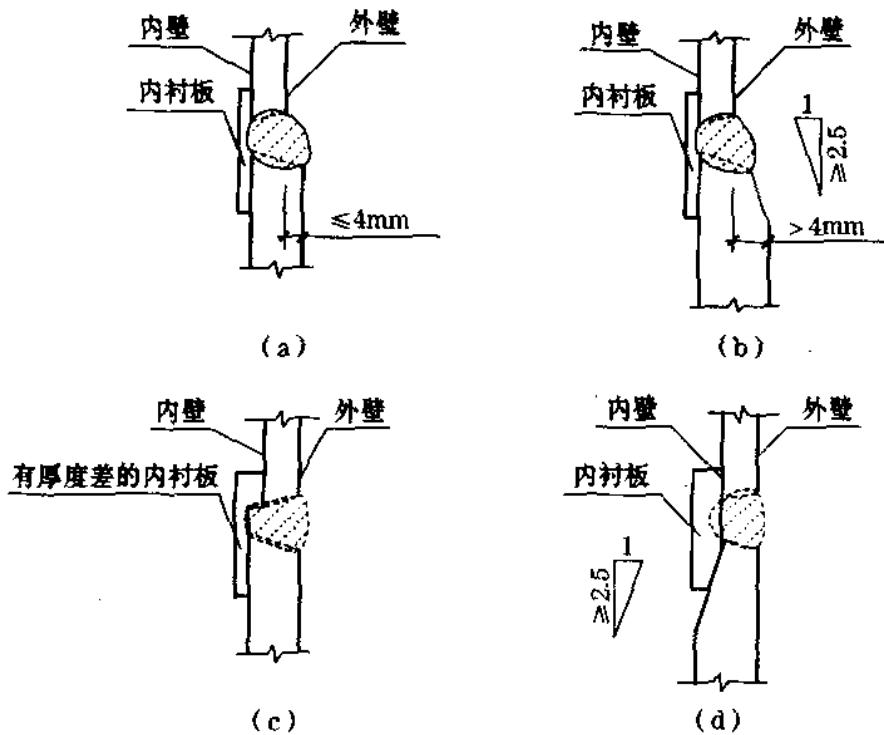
不同壁厚钢管的工厂焊接
